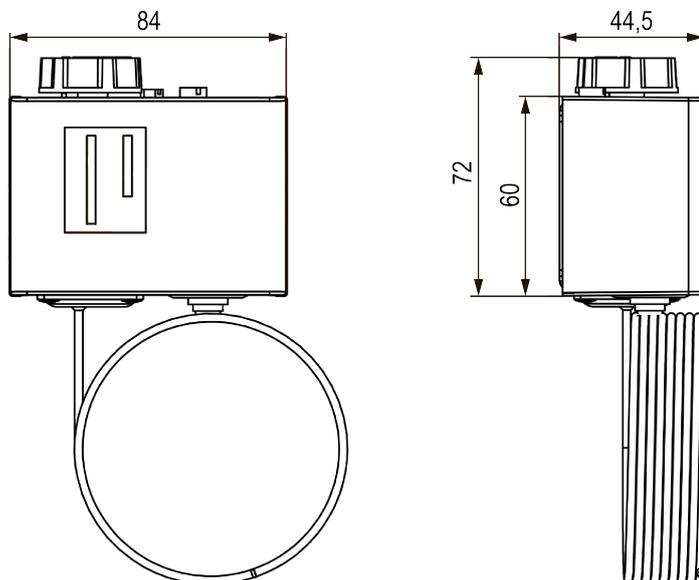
Габаритные и присоединительные размеры реле
